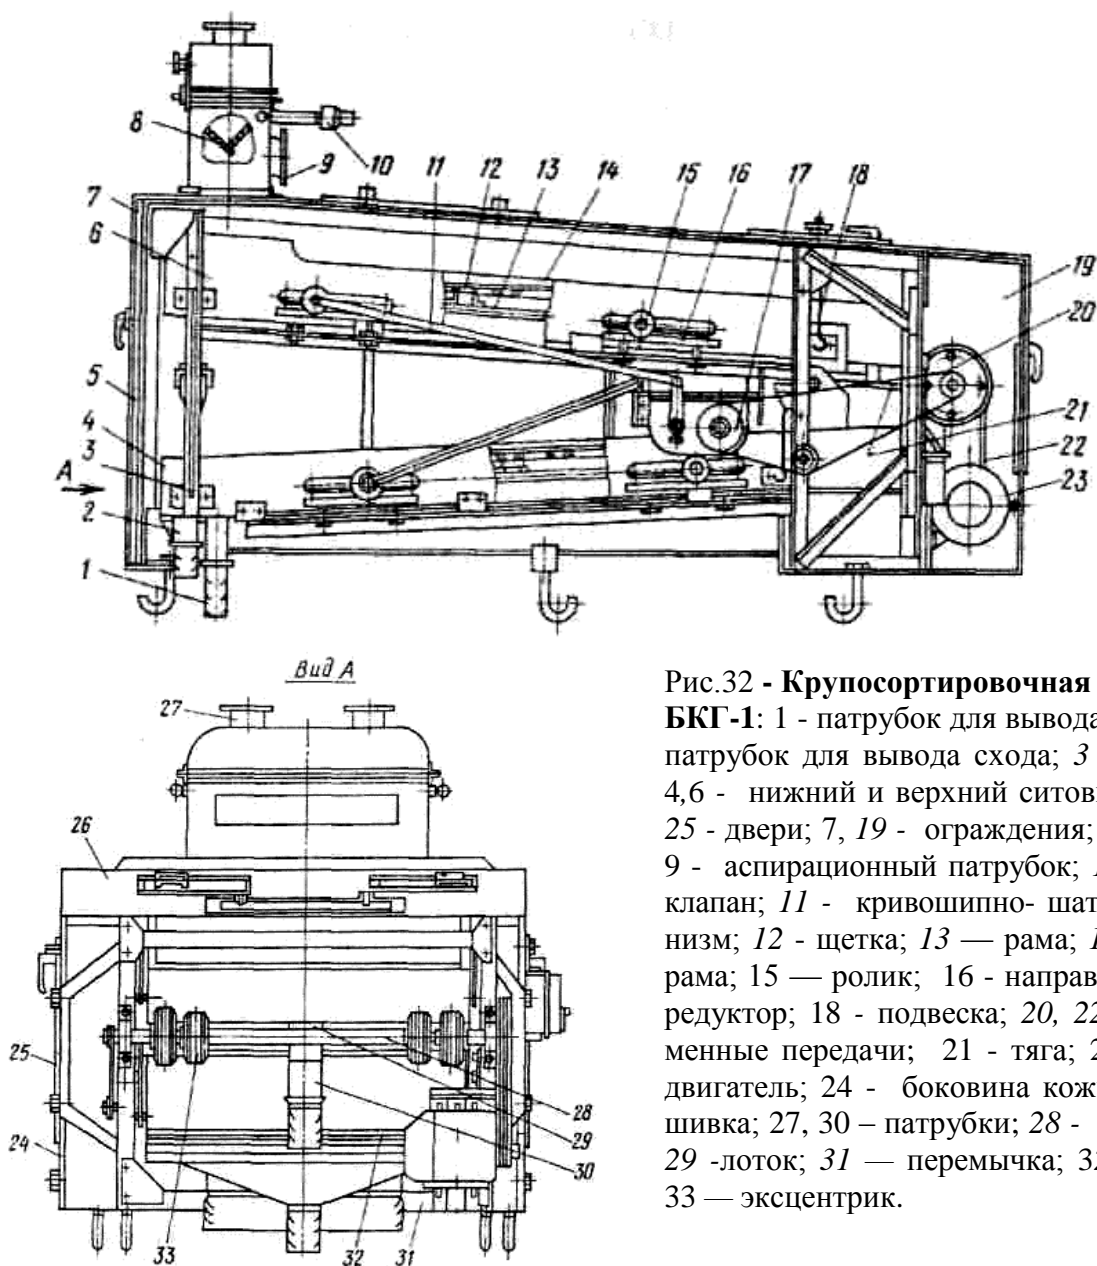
Крупосортировочная машина А1-БКГ-1: 1 - патрубок для вывода прохода; 2 - патрубок для вывода схода; 3 - боковина; 4,6 - нижний и верхний ситовые кузова; 5, 25 - двери; 7, 19 - ограждения; 8 - питатель; 9 - аспирационный патрубок; 10 - грузовой клапан; 11 - кривошипно-шатунный механизм; 12 - щетка; 13 — рама; 14 — ситовая рама; 15 — ролик; 16 - направляющая; 17 - редуктор; 18 - подвеска; 20, 22 - клиноременные передачи; 21 - тяга; 23 - электродвигатель; 24 - боковина кожуха; 26 - обшивка; 27, 30 - патрубки; 28 - главный вал; 29 - лоток; 31 — перемычка; 32 — поддон; 33 — эксцентрик.
